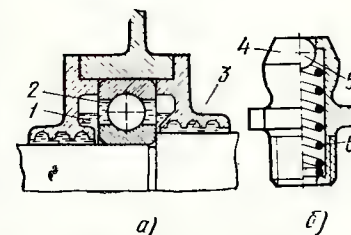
Размещение смазки в подшипниковой опоре (а) и шариковая пресс-масленка (б)
